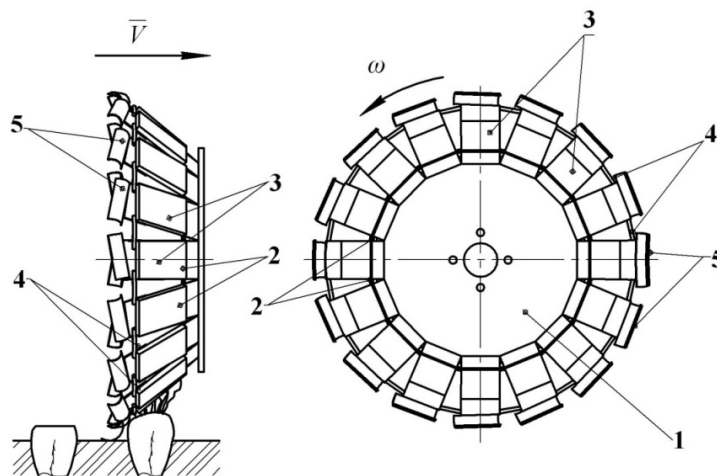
Конструкційна схема нового копірно-роторного відокремлювача гички
